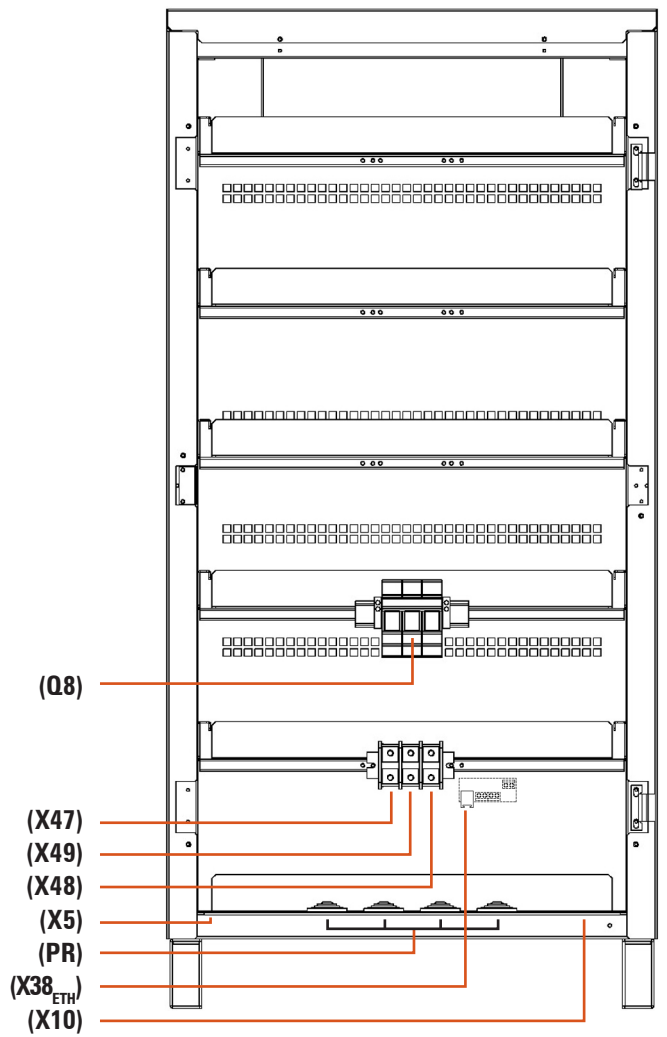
Vista frontal armario baterías N° 2, con puerta abierta.
